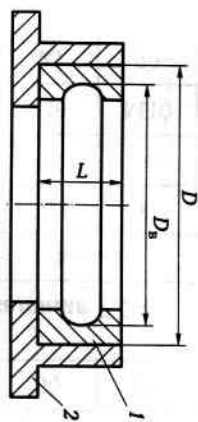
Схема запрессовки наружного кольца 1 подлинника в корпус 2
